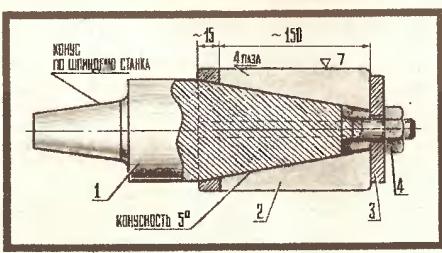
Притир для обработки цилиндра: 1 — оправка; 2 — чугунная разрезная втулка; 3 — шайба; 4 — гайка.
